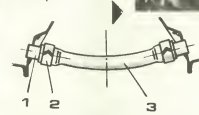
Крепление бензинового шланга: 1 — штуцер; 2 — зажим; 3 — шланг.
